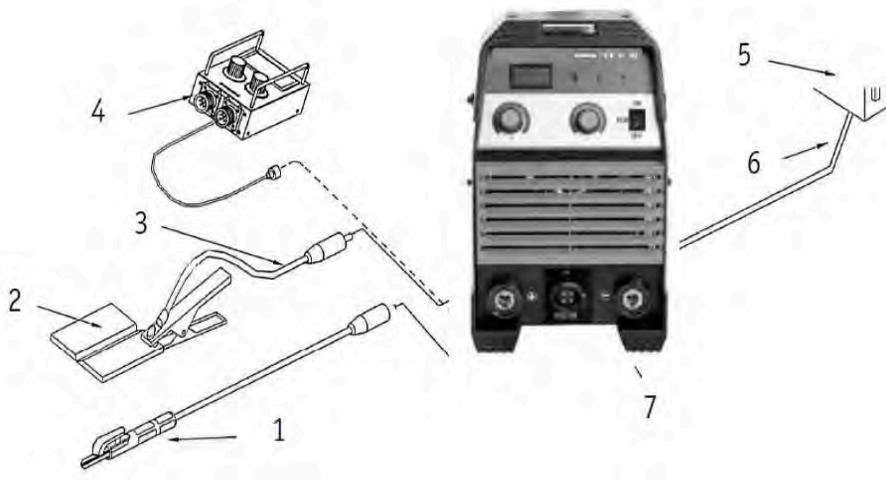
Схема подключения оборудования для ММА сварки
